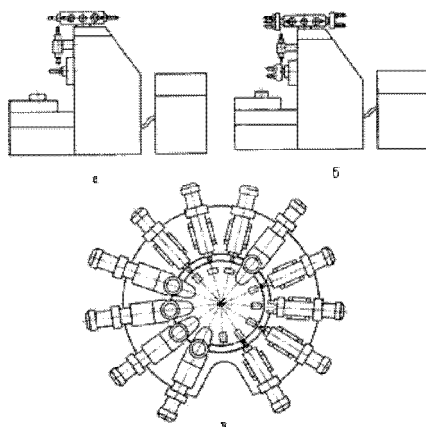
Варіанти концентрації переходів на верстатах: а - обробний центр із магазином інструментів; б - обробний центр із магазином інструментів і багатошпindelних коробок; в - багатопозиційний агрегатний верстат
